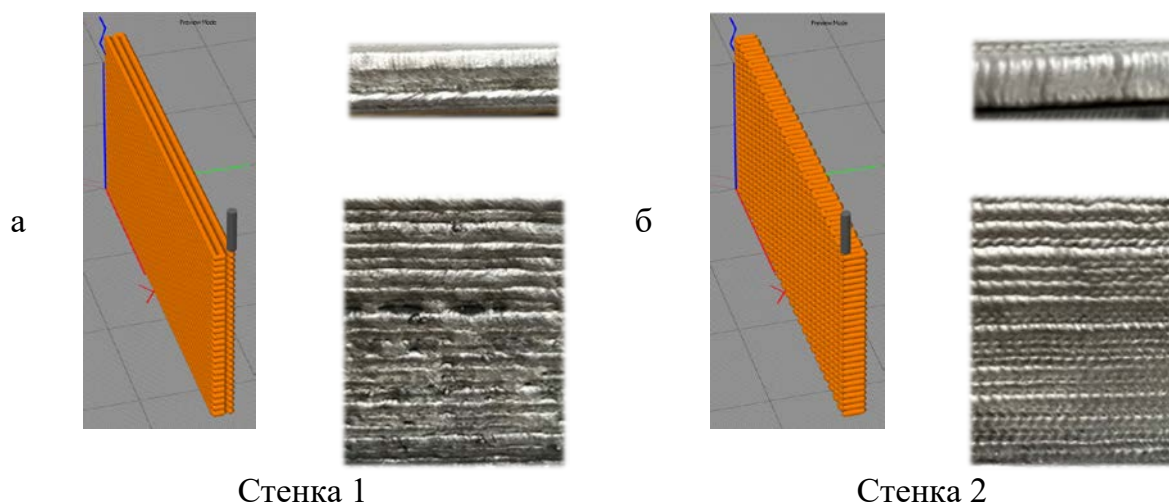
Стратегии наплавки: а) продольно-параллельная; б) с поперечной осцилляцией. Внешний вид боковой и верхней поверхностей наплавленных стенок
